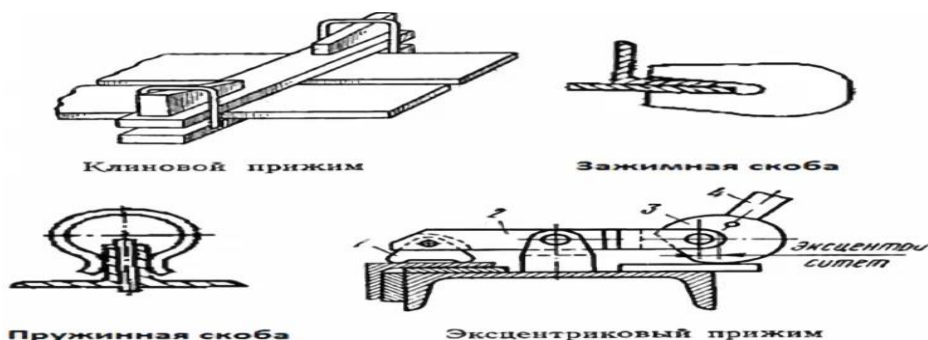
Переносные приспособления для сборочно-сварочных работ.
